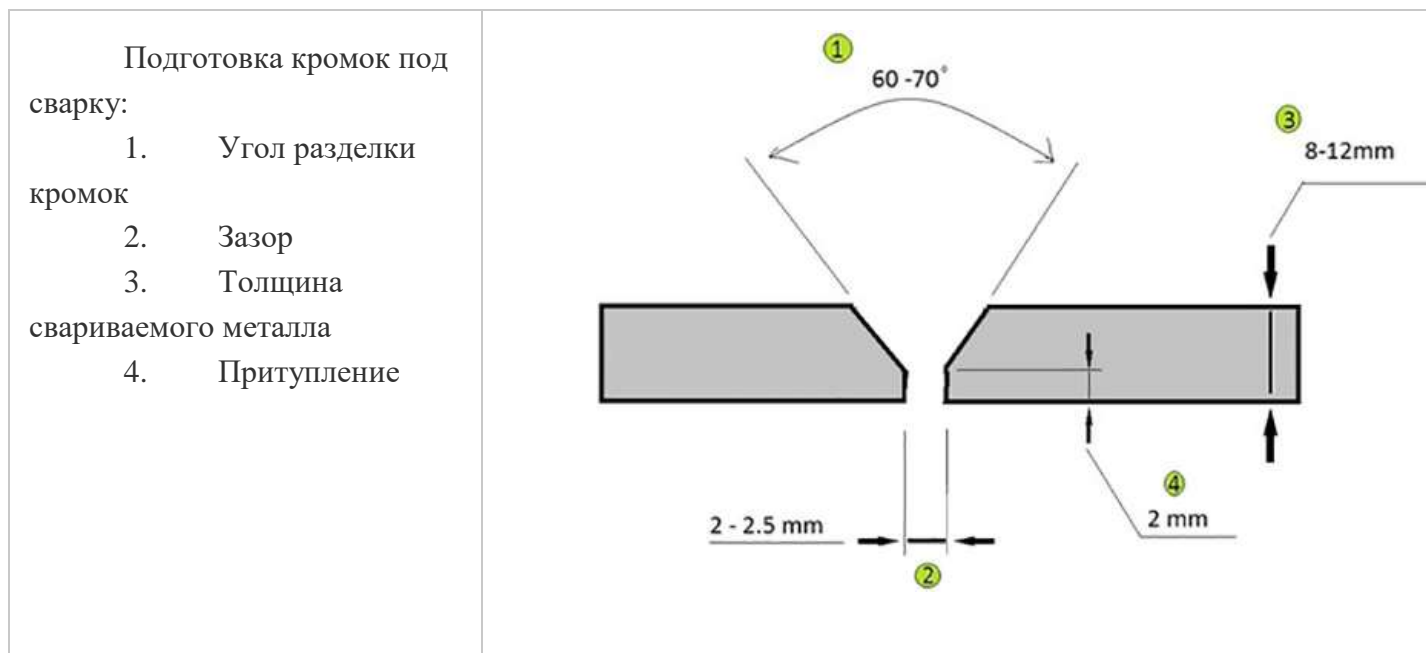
Подготовка кромок труб под сварку при толщине стенок 8...12 мм
